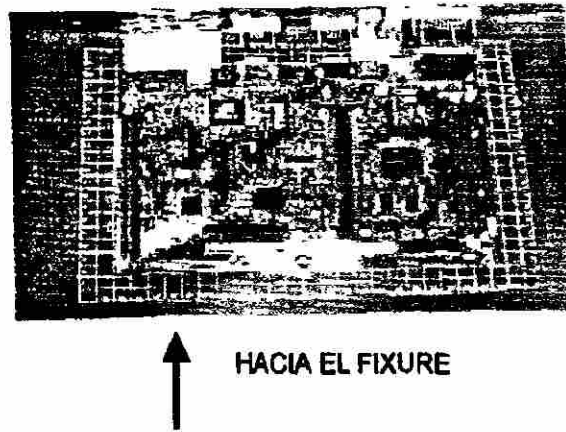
Posicionamiento de la "PCB" en el "fixure"
